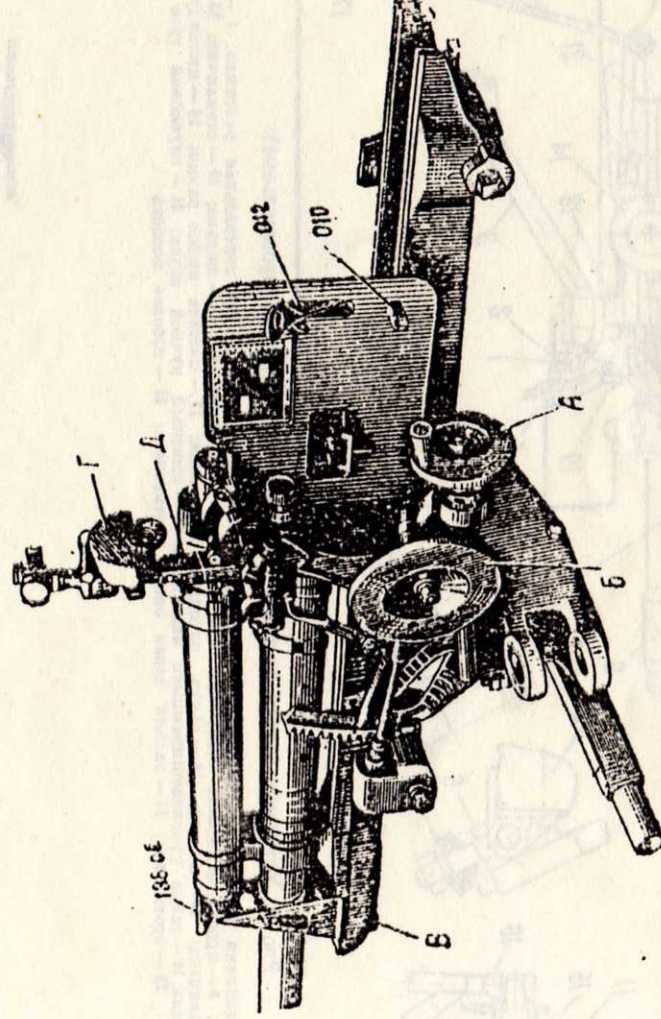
Вращающаяся часть орудия с лобовой коробкой и боевой осью (вид слева):
